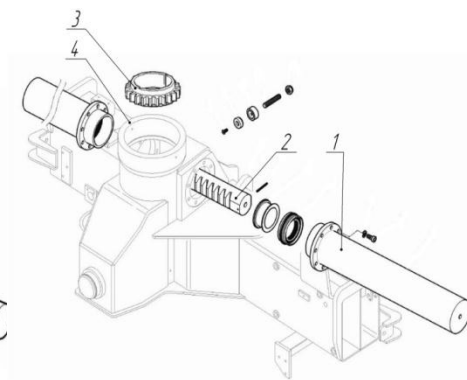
Опорно-поворотний пристрій на основі гідроциліндра та рейки
